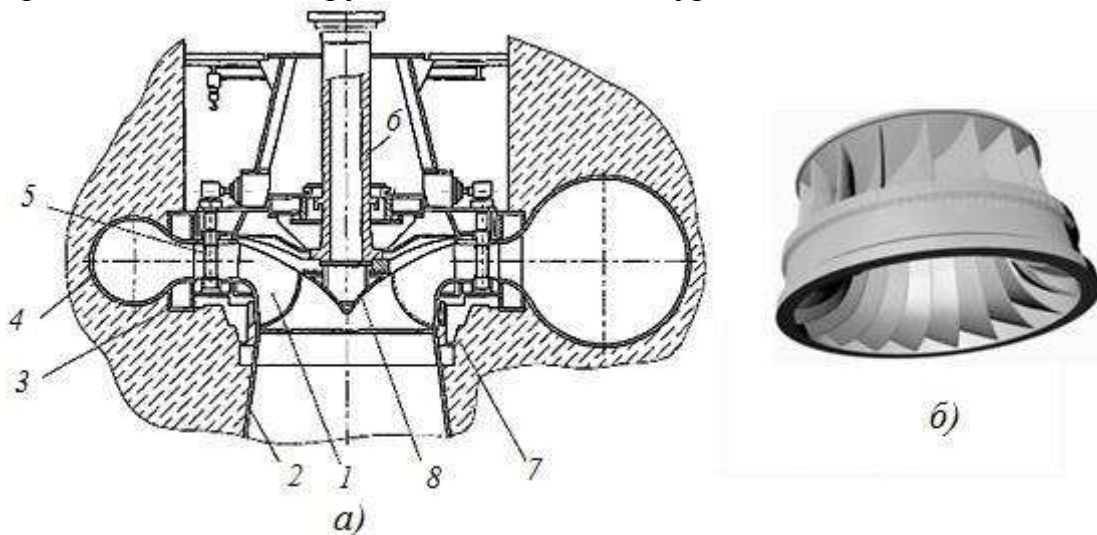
Схема(а) та загальний вигляд робочого колеса(б) радіально-осьової турбіни: 1 – робоче колесо; 2 – відсмоктувальна труба; 3 – статор; 4 – спіральна камера; 5 – лопатки направляючого апарату; 6 – вал; 7 – колектор; 8 – конус робочого колеса
